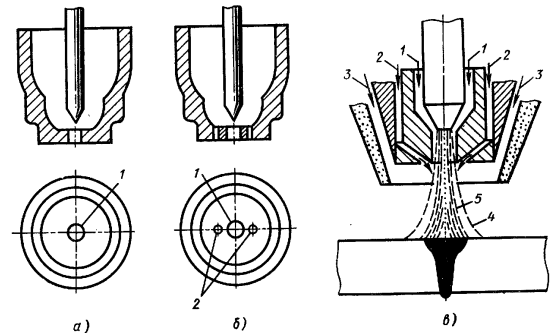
Схемы плазмобразующих сопел для сварки плазменной дугой:
